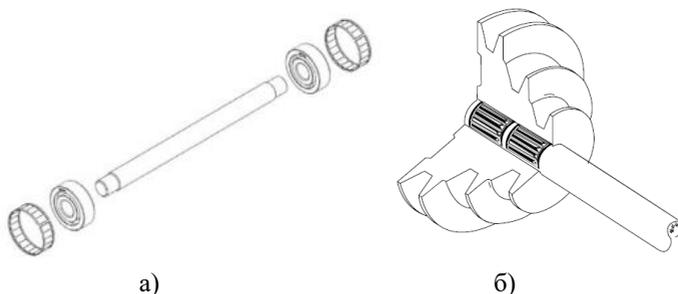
Крепление опор подшипников (а), крепление шкива (б).
